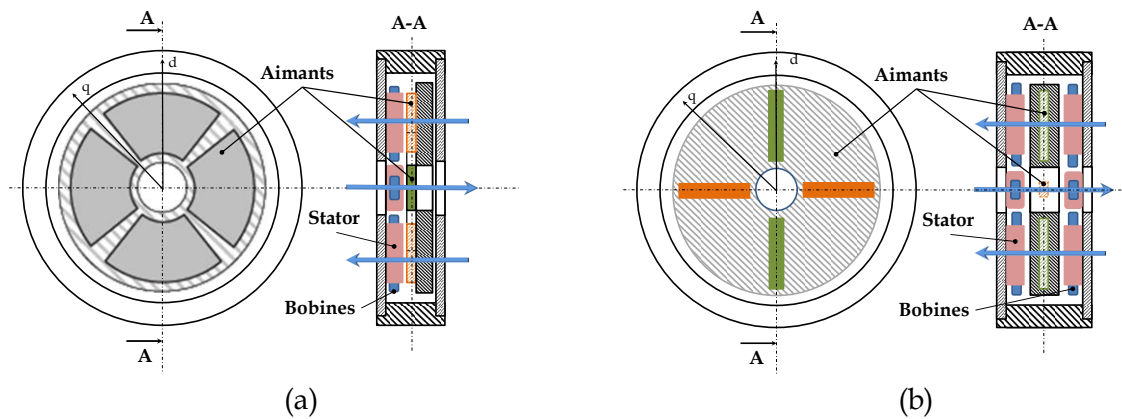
Machines à aimants à flux axial- (a) surfacique - (b) enterrés
